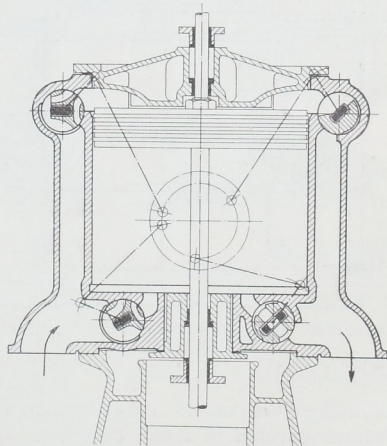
Zylinder für stehende Maschine nach Doerfel.
